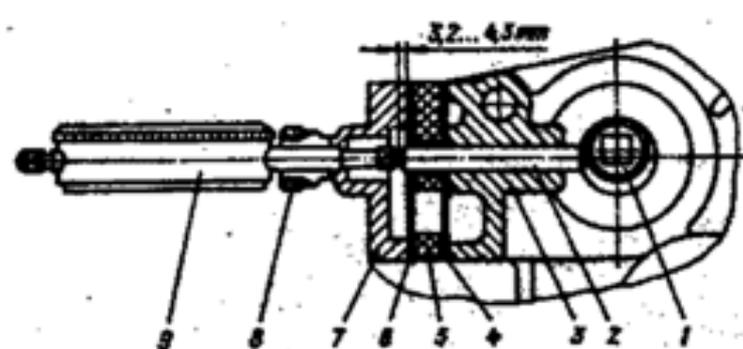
Приспособление для замера выступающей штанги привода безшарикового насоса: 1 - приводной кулачок; 2 - штанга; 3 - корпус привода; 4 - уплотнительно-регулирующие прокладки; 5 - проставка; 6 - уплотнительная прокладка; 7 - фланец; 8 - гайка цапговая; 9 - индикатор
